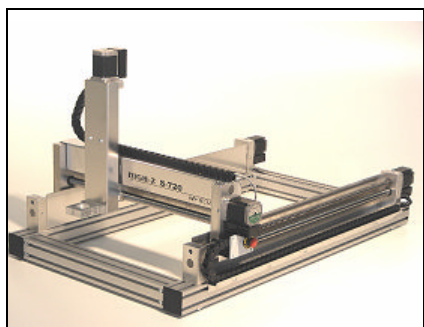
Fräsmaschine der Fa. CNC-Step [1]
